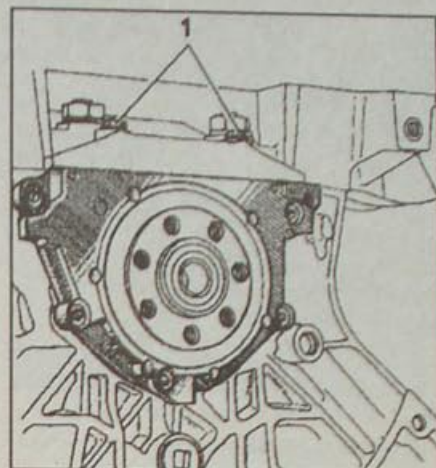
Расположение двух нижних болтов (1) крепления задней крышки блока цилиндров, которые необходимо затягивать в первую очередь
